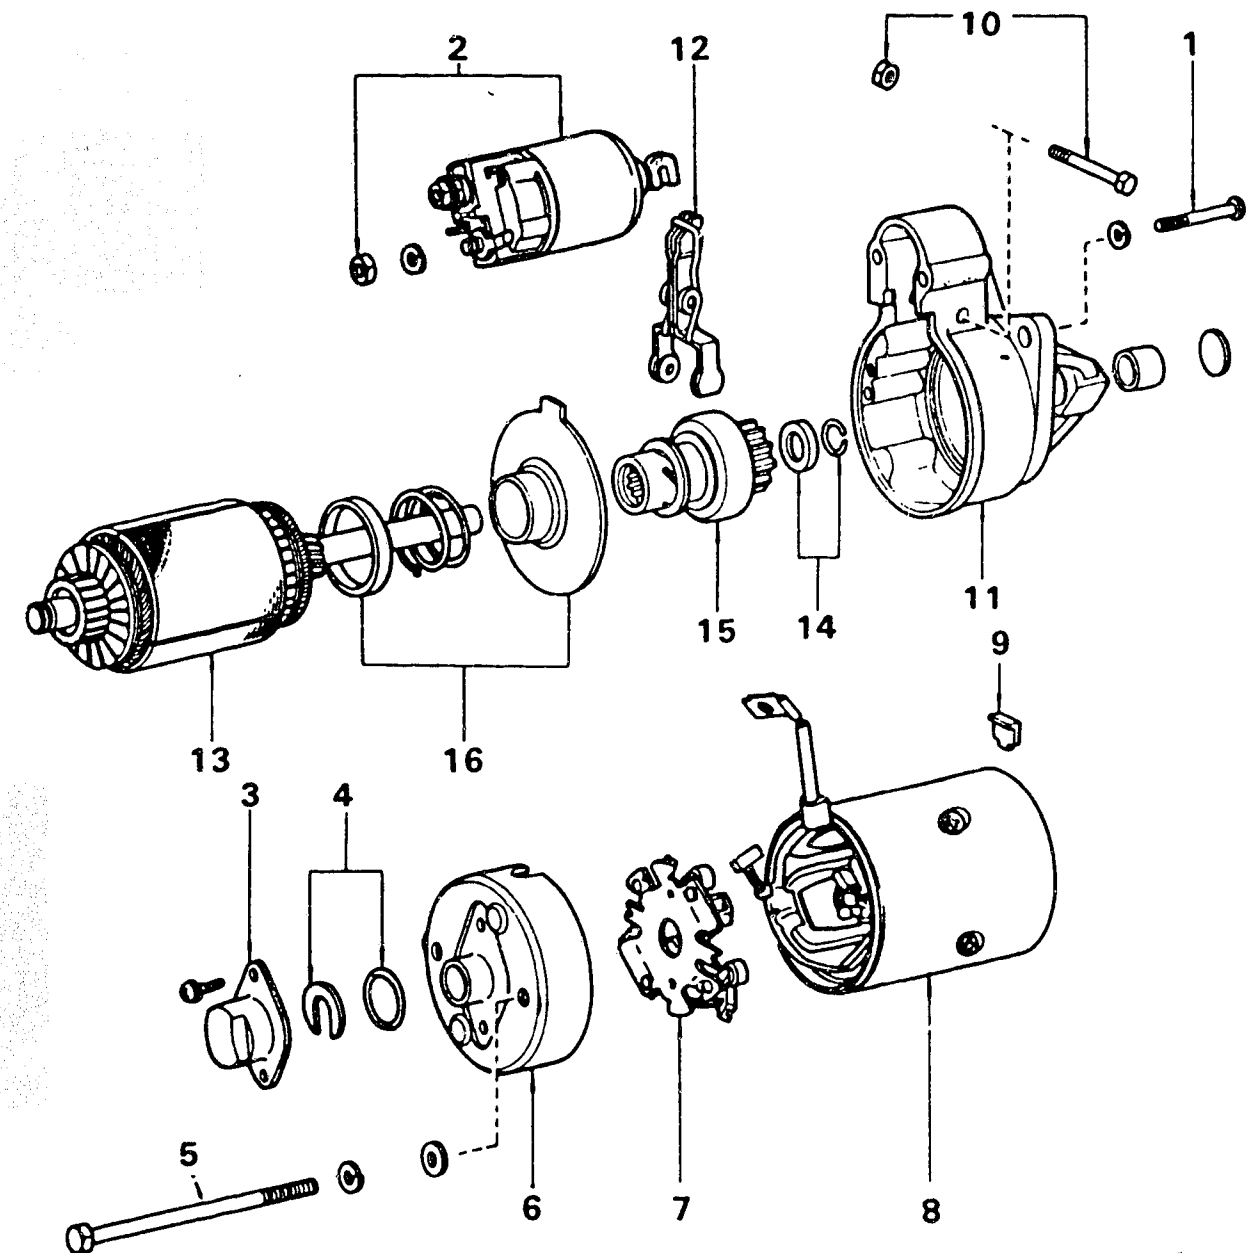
Dieser Starter ist im Motor 21R/21R-C eingebaut. 1 Befestigungsschraube des Magnetschalters – 2 Magnetschalter – 3 Lagerdeckel – 4 O-Ring, Halteplatte und Gummischeibe – 5 Schraube – 6 Kommutatorabdeckung – 7 Bürstenhalter – 8 Polgehäuse – 9 Dichtung – 10 Schraube und Mutter – 11 Antriebsgehäuse – 12 Einrückhebel – 13 Anker – 14 Sicherungsring und Anlaufhülse – 15 Freilaufkupplung mit Ritzel – 16 Feder, Federteller und mittleres Lager.
